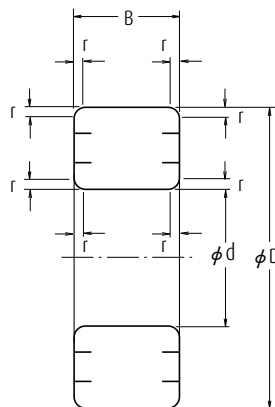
Dimensiones Globales para Rodamientos de Bolas y de Rodillos
